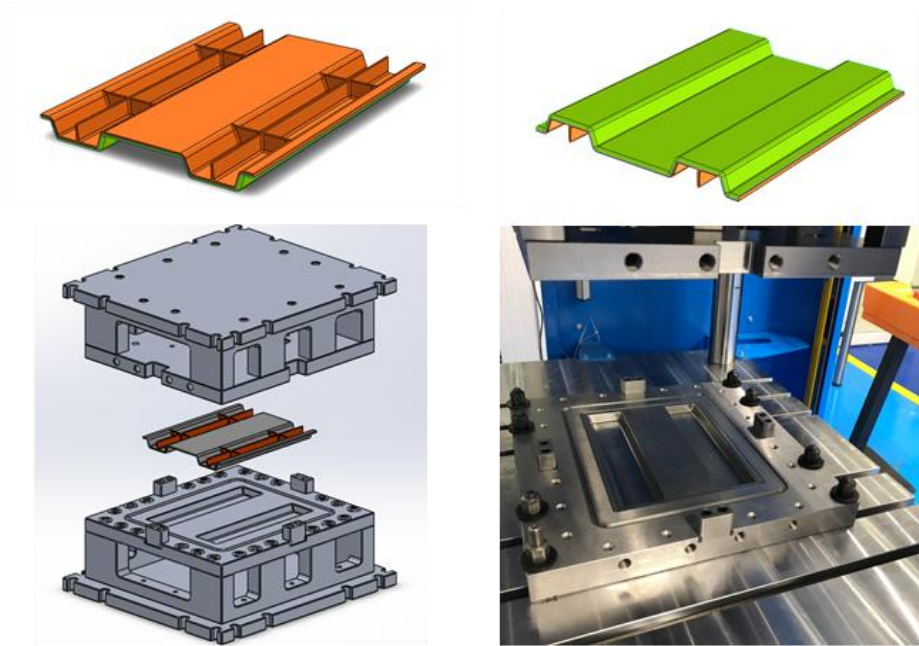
Geometría del molde y componente para la integración de refuerzo de impresión 3D – cFF por sobremoldeo de GMT.
